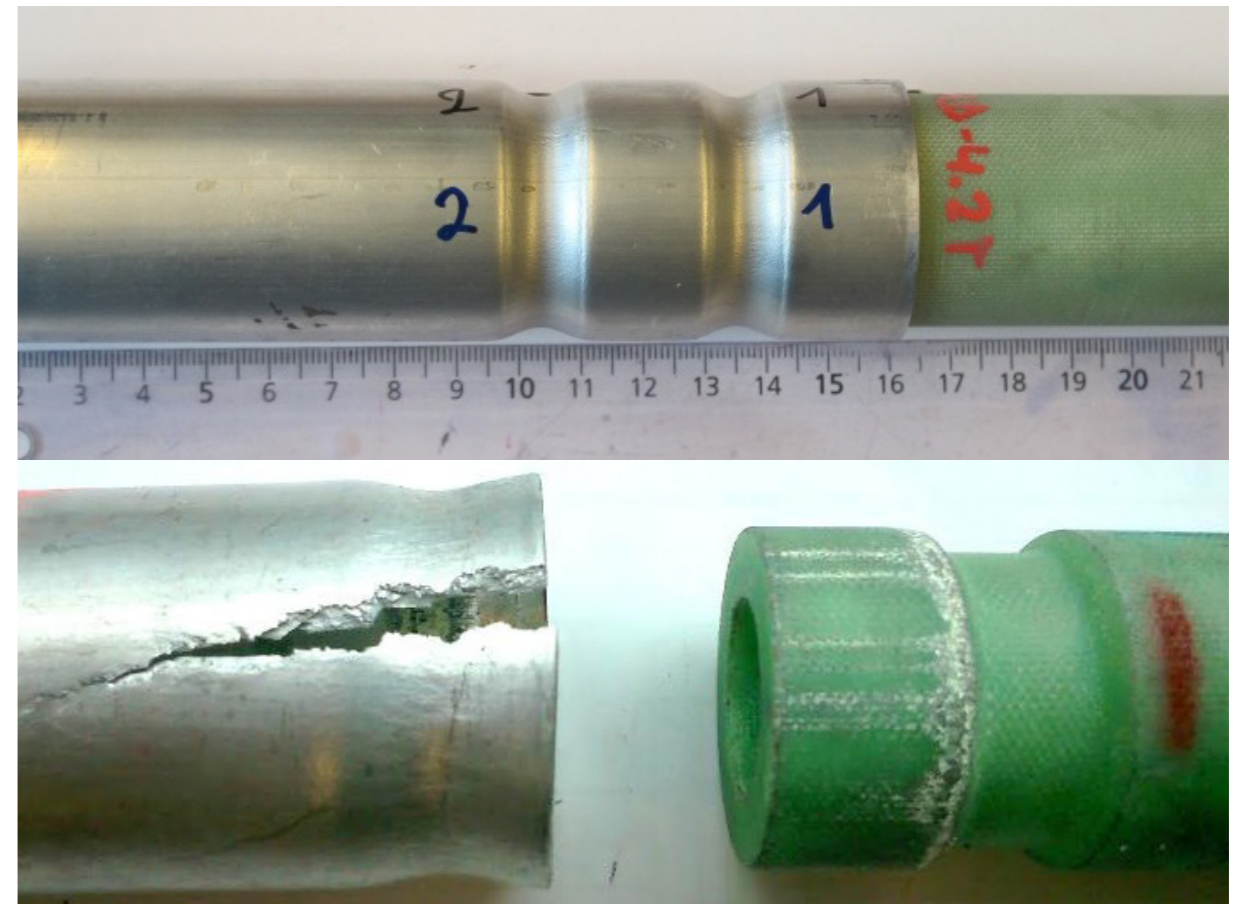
Assemblage d'un tube en aluminium EN AW-6082 T6 et d'une pièce composite GC22, avant et après exécution d'un test de traction
